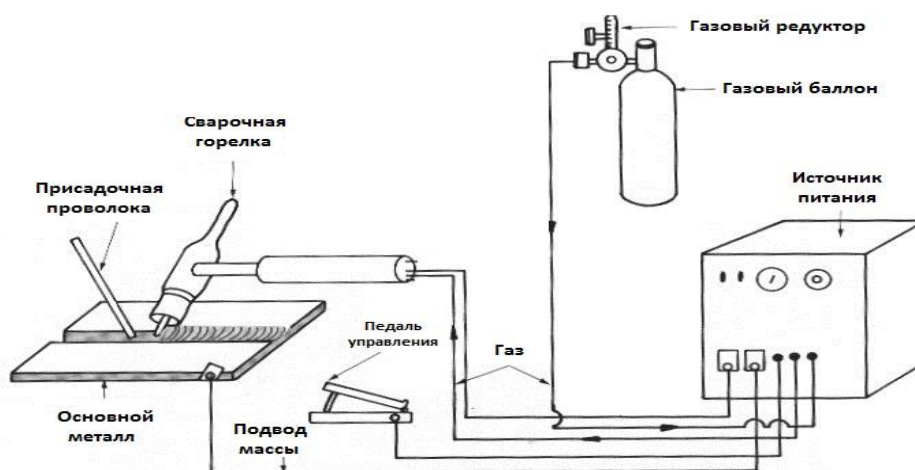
Сварка неплавящимся электродом в среде инертного газа.
